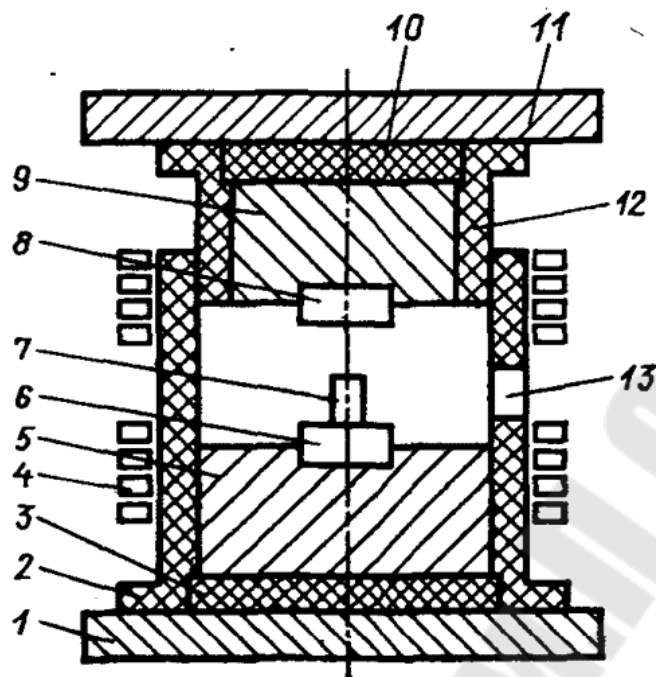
Принципиальная схема штампового блока для изотермической штамповки: 1 - нижняя опорная плита; 2 - нижний подвижный кожух; 3 - нижняя прокладка; 4 - индуктор; 5 - нижний штамподержатель; 6 - нижний штамп; 7 - заготовка; 8 - верхний штамп; 9 - верхний штамподержатель; 10 - верхняя прокладка; 11 - верхняя опорная плита; 12 - кожух; 13 - окно
